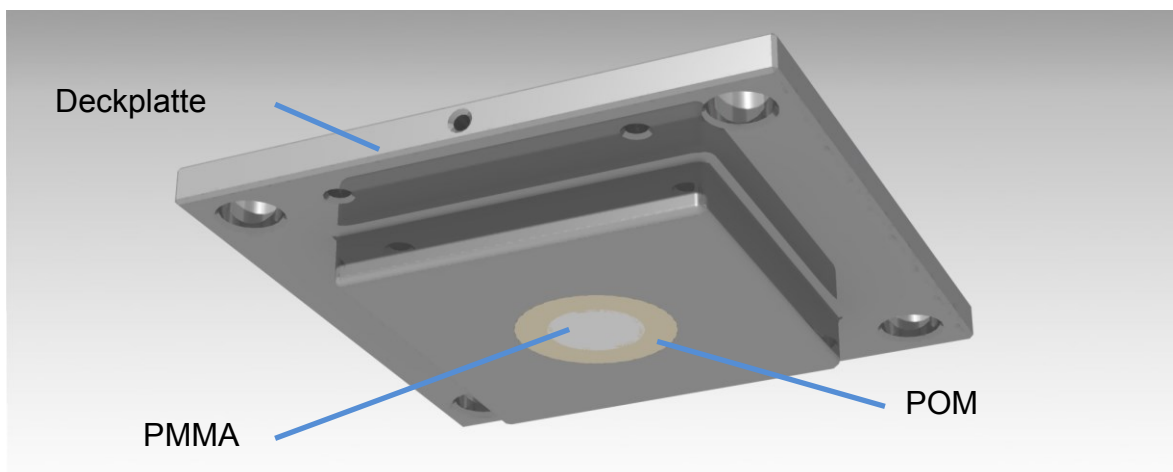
Deckplatte mit Sicht von unten. Mittig ist der Adapter für die US Aufnahme zu erkennen.
